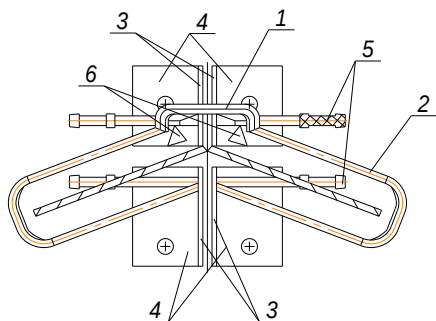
Индуктор для одновременной наплавки носовой части стрелчатой лапы и закалки ее крыльев:
